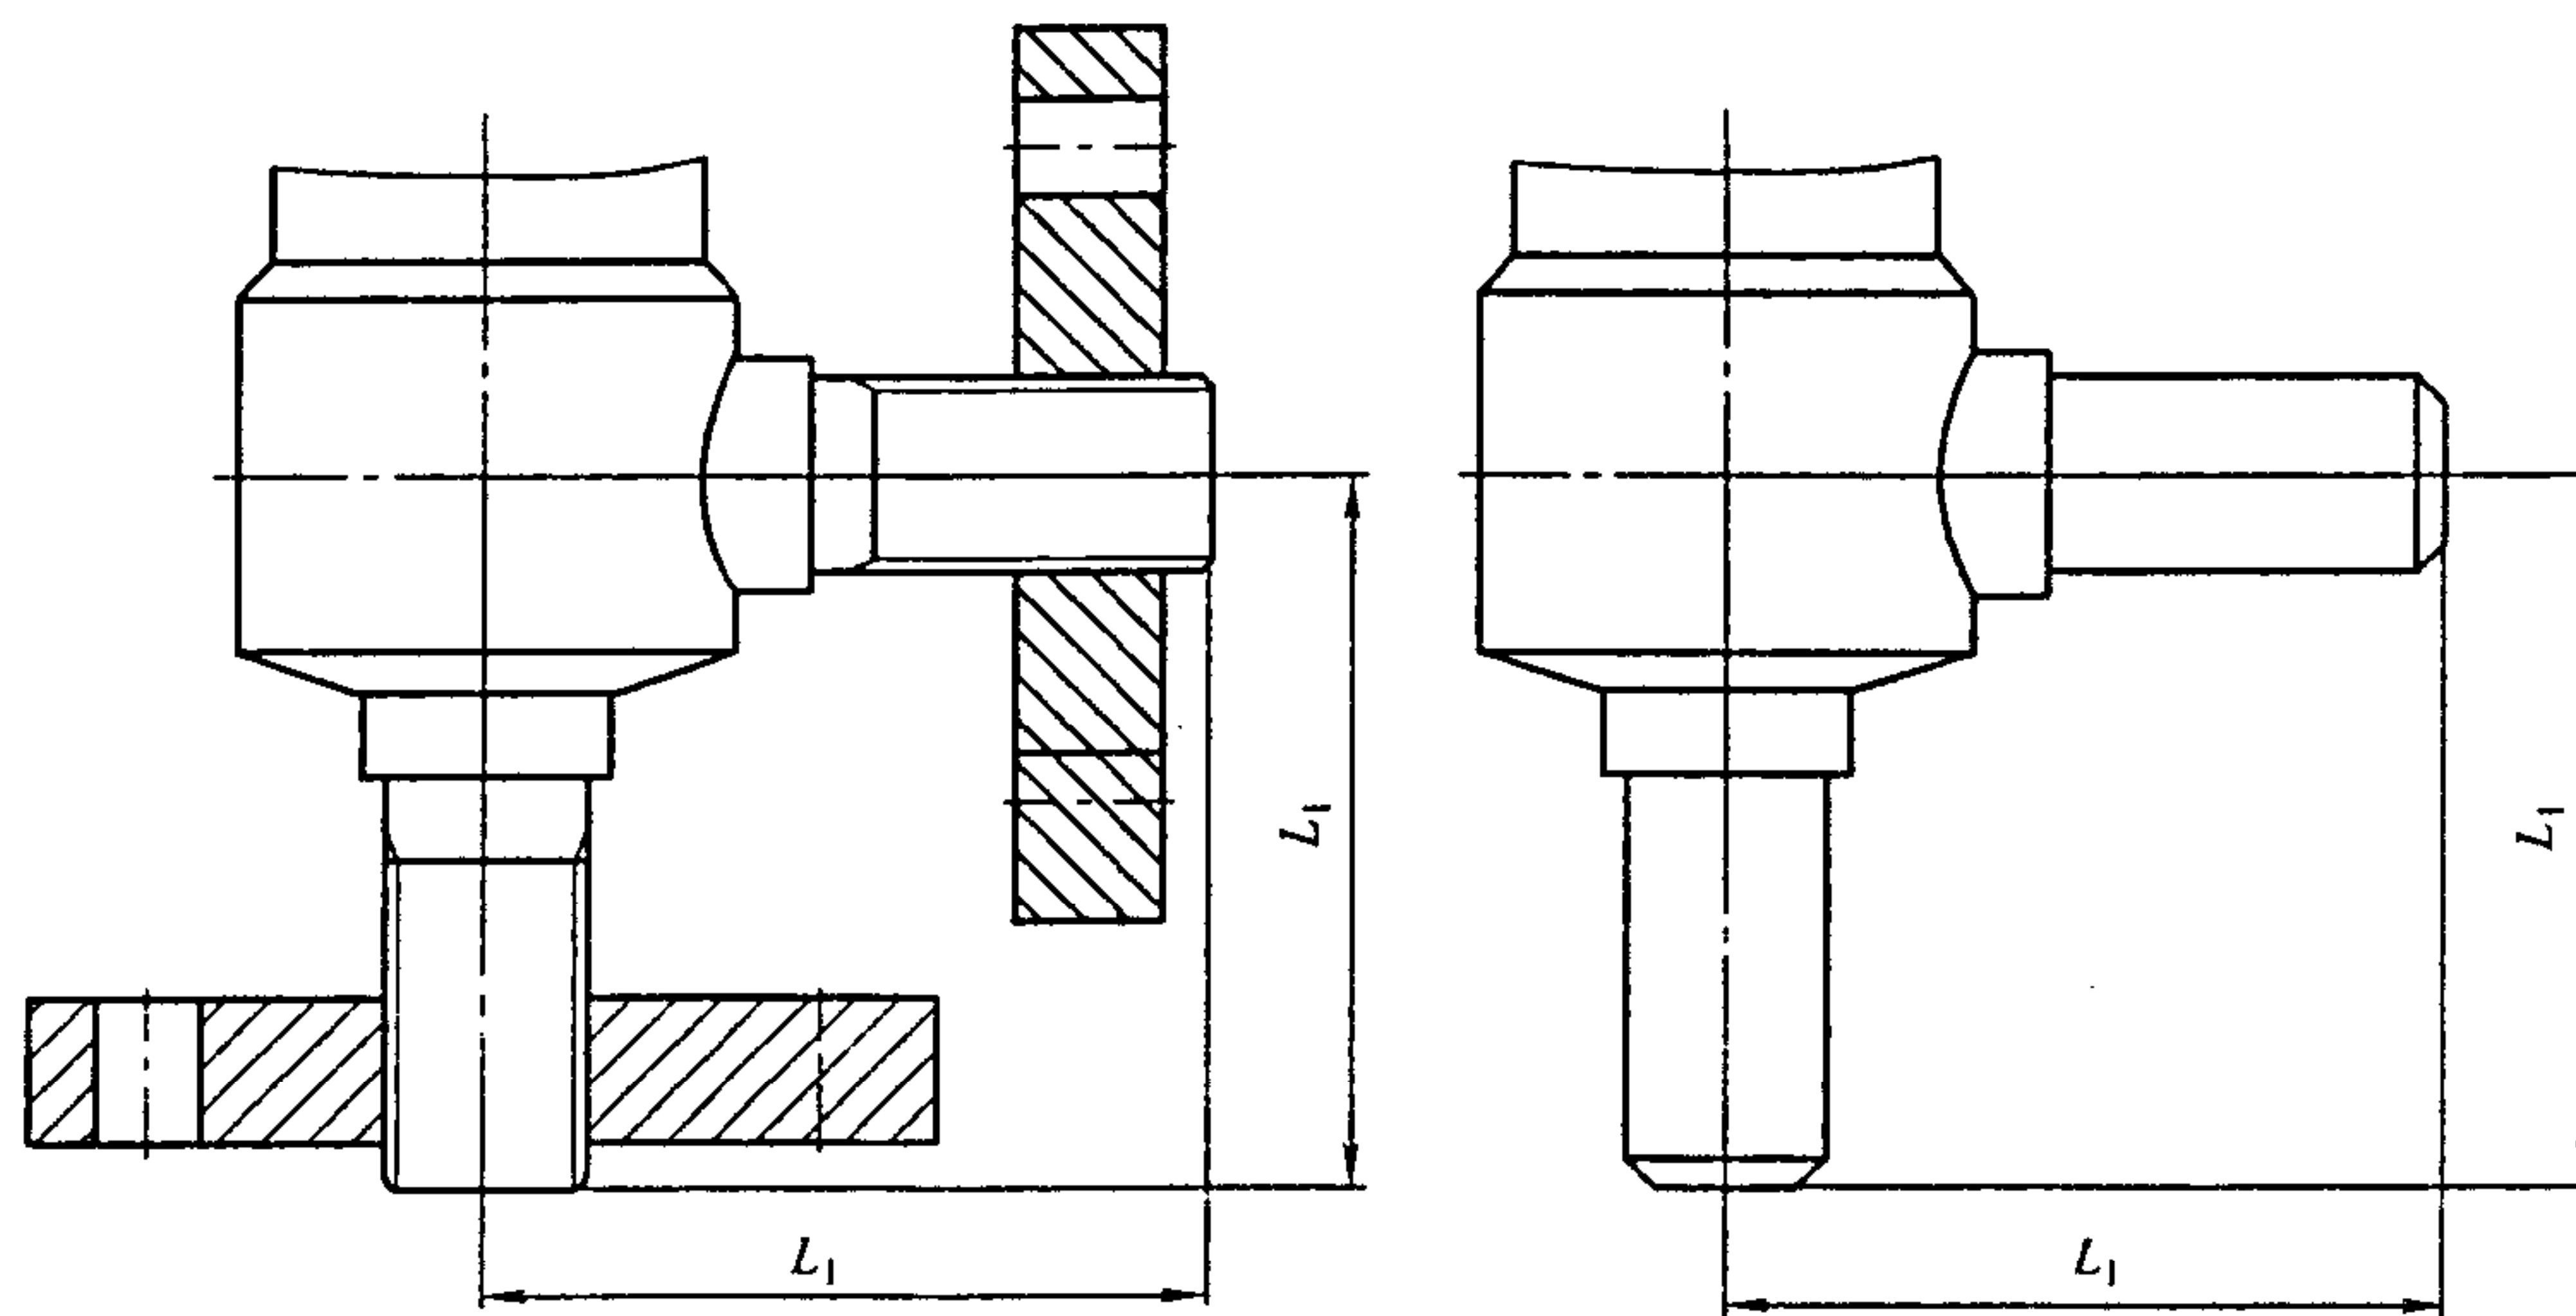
螺纹法兰和焊接连接的角式截止阀的结构长度示意图
